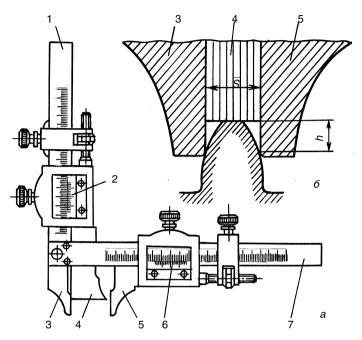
Хордовый зубомер: а — общий вид схемы измерения; б — схема измерения
